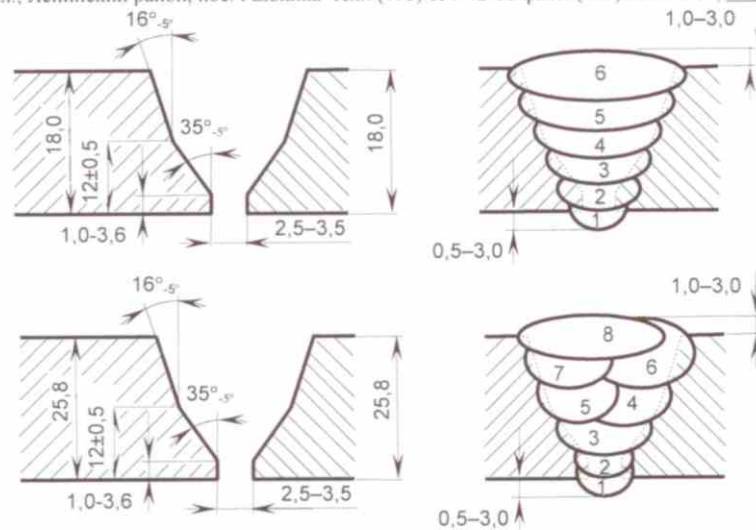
Геометрические параметры сборки и эскиз сварных швов КСС $\varnothing 1220 \times 18,0$ мм класса прочности К52 и $\varnothing 1420 \times 25,8$ мм класса прочности К60, сваренных по технологии автоматической односторонней сварки проволокой сплошного сечения под флюсом
